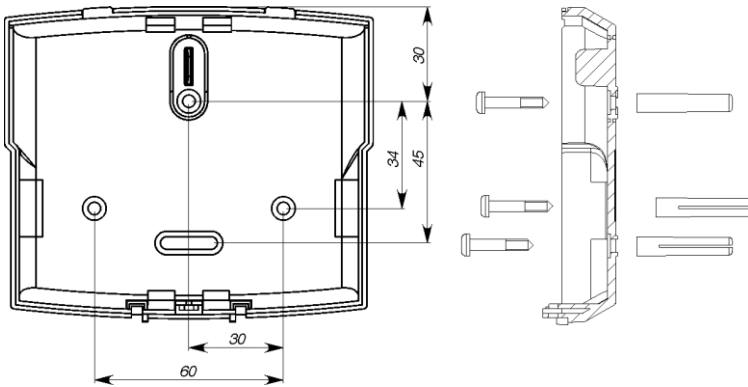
Разметка крепежных отверстий для клавиатуры M4064KP
